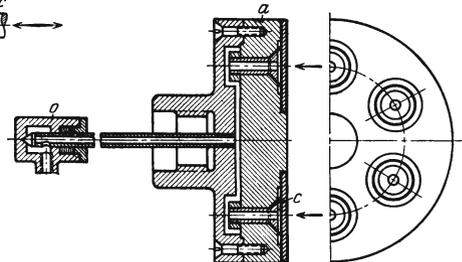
Vakuumspanner für Rundbearbeitung. a = Umlaufender Spannkörper. b = Feststehender Saugluftanschlußkörper. c = Gummilufttaschen.
